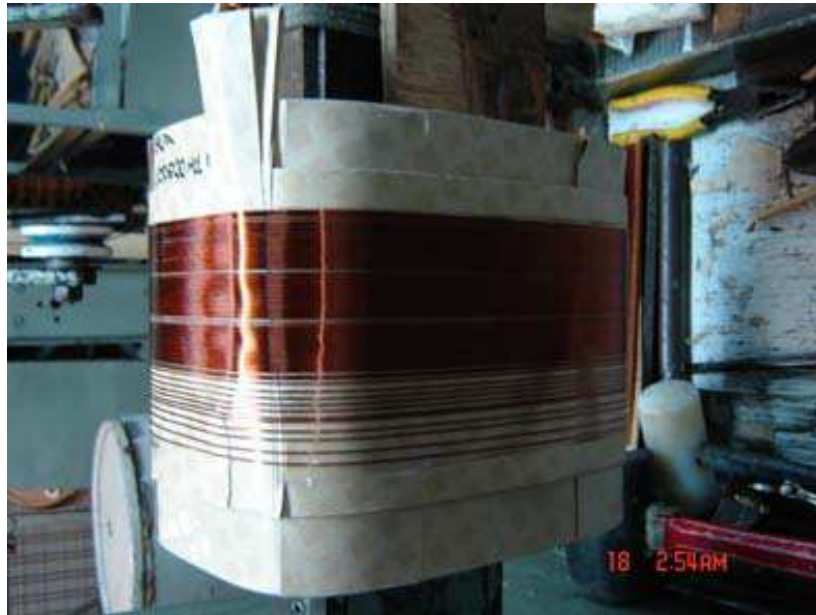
Montaje de los hilos de cobre de la primera capa del bobinado de alta tensión.
